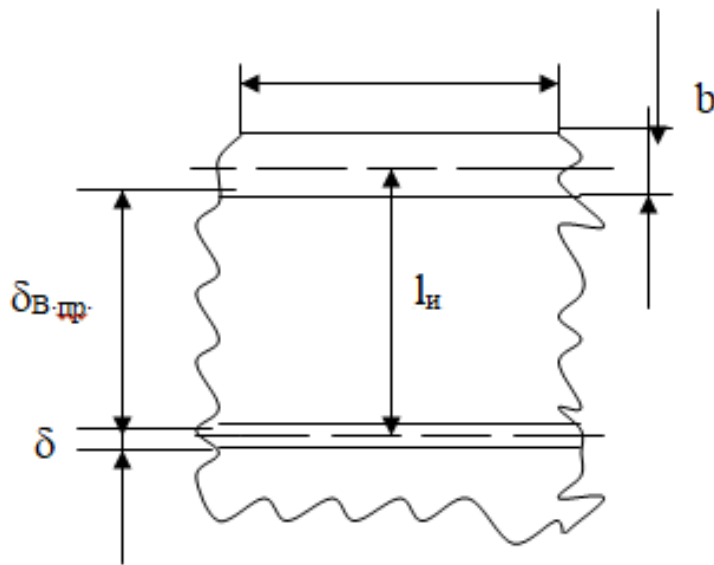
Схема розташування небезпечної зони біля розливного жолоба
